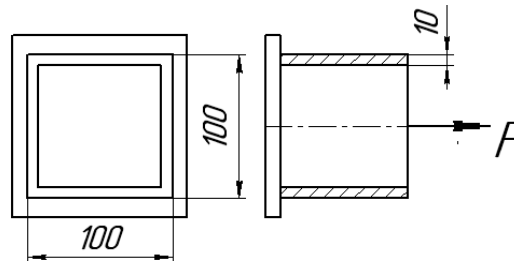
Сварное соединение трубы квадратного сечения, выполненное тавровыми сварными швами
